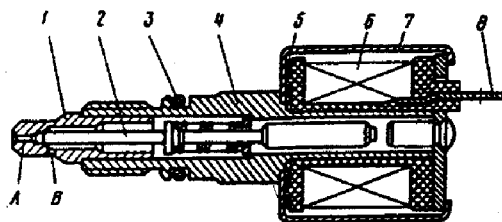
Válvula de corte: 1 - gargulante de marcha-lenta; 2 - agulhas; 3 - anel de vedação; 4 - corpo da válvula; 5 - placa de contato; 6 - bobina; 7 - armadura da bobina; 8 - terminal; A - orifício calibrado do gargulante; B - orifício de saída do combustível.
